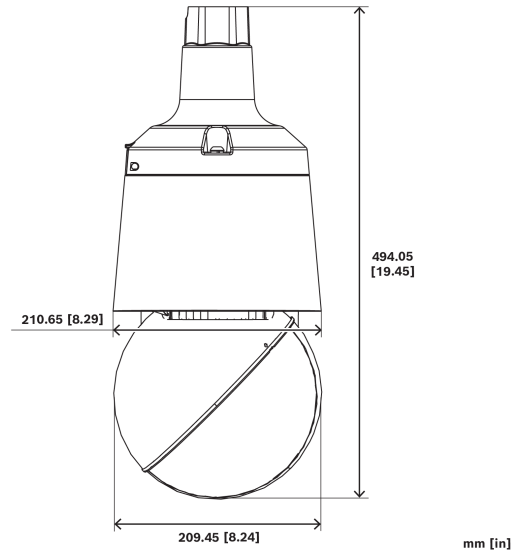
Dimensões em mm (pol.) de câmera instalada em NDA-7100-PIPE | NDA-7100-PIPEF (suporte de tubo)
